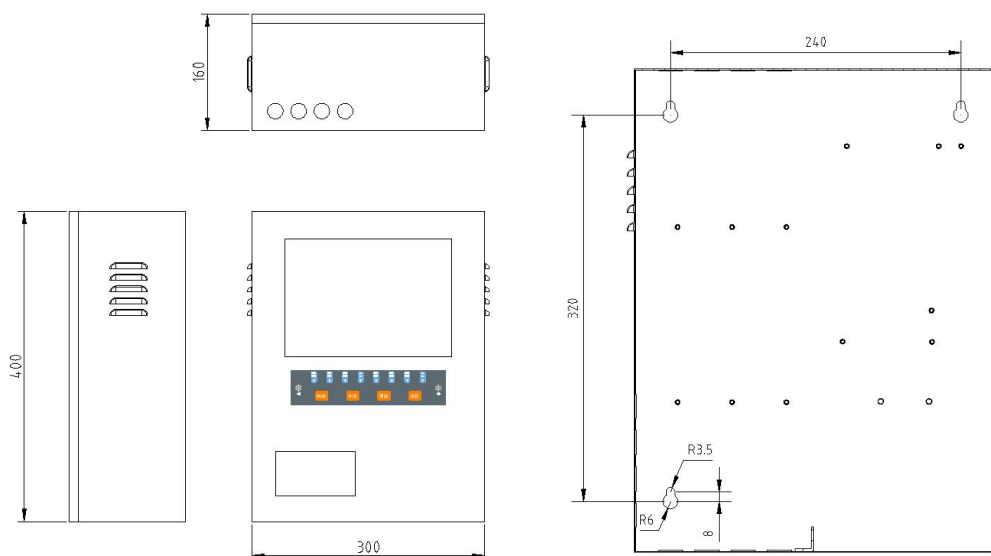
A-C-A100/B3 型应急照明控制器外形尺寸图和安装尺寸图
